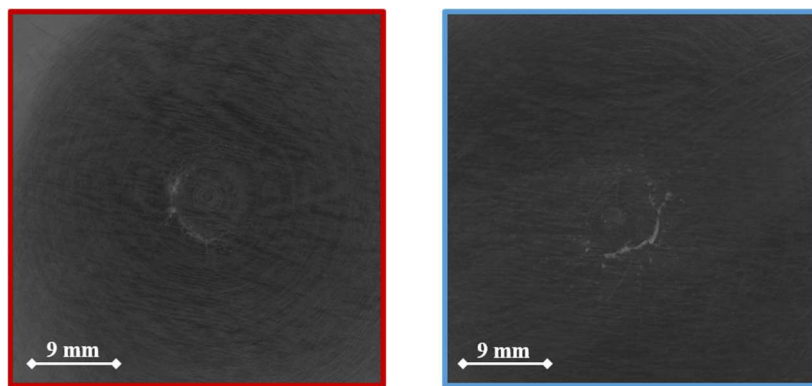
Photos des faces de l'éprouvette 743B-N en fin d'essai
